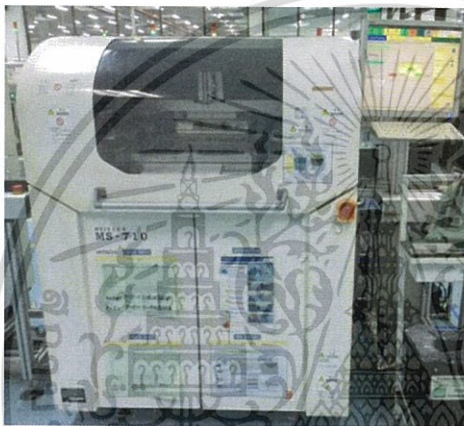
Solder Paste Printing Vender คือ DEK
